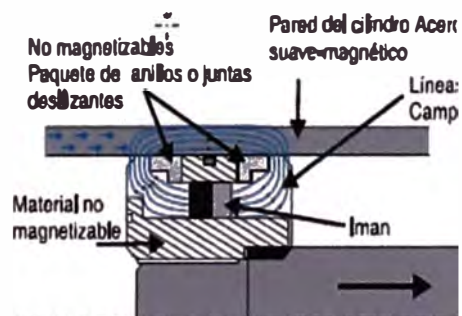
Representación del sensor en el pistón como generador de campo.
